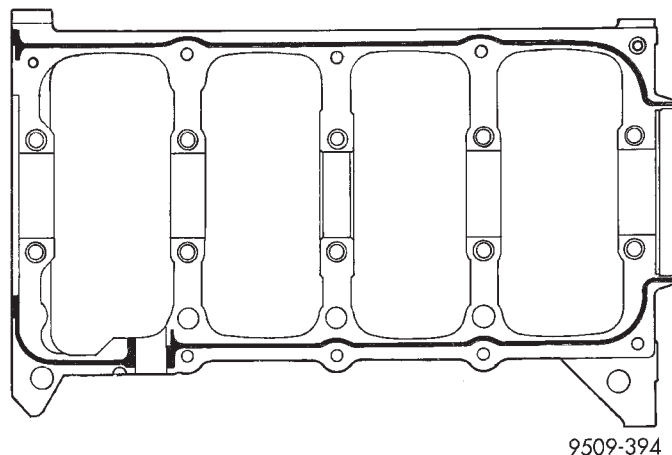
Sellado de las tapas del cojinete principal/bancada
